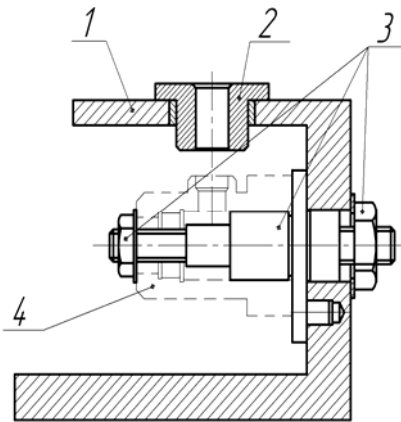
Групповое переналаживаемое приспособление где: 1 – корпус; 2 – сменная втулка; 3 – сменный комплект (оправка, элементы крепления и ориентирования); 4 – контур детали
